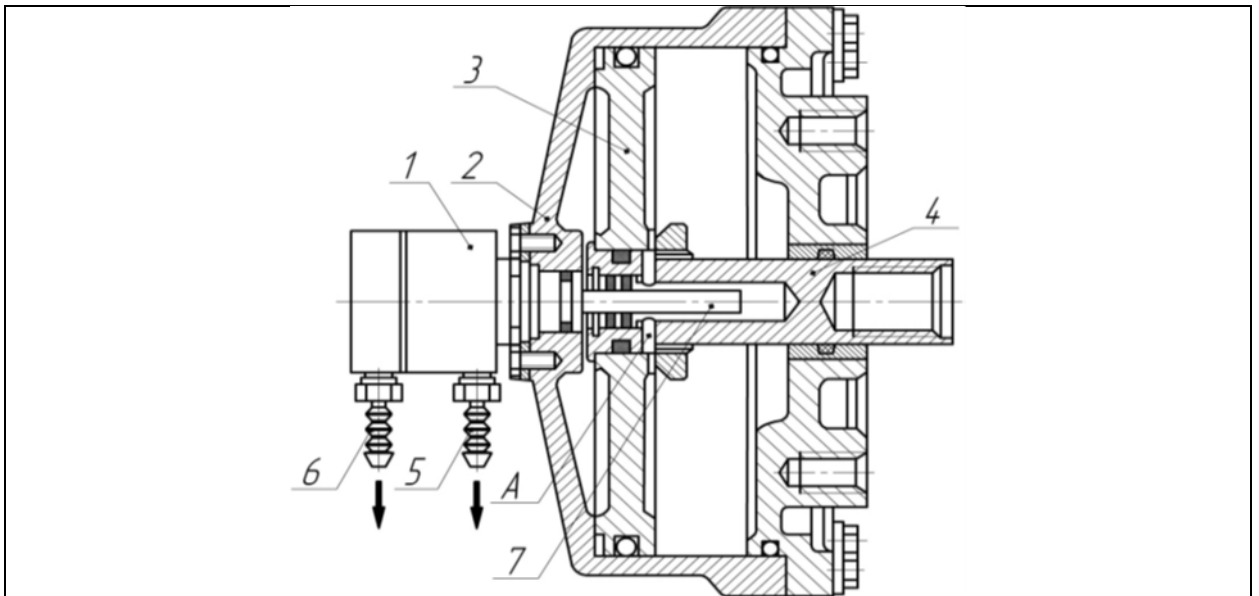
Конструкція пневматичного циліндра, що обертається, з нерухомою муфтою для підведення стисненого повітря: 1-муфта для підведення стисненого повітря; 2-циліндр; 3-поршень; 4-шток; 5,6-штуцери; 7-стрижень (трубка) для підведення стисненого повітря в штокову порожнину.
